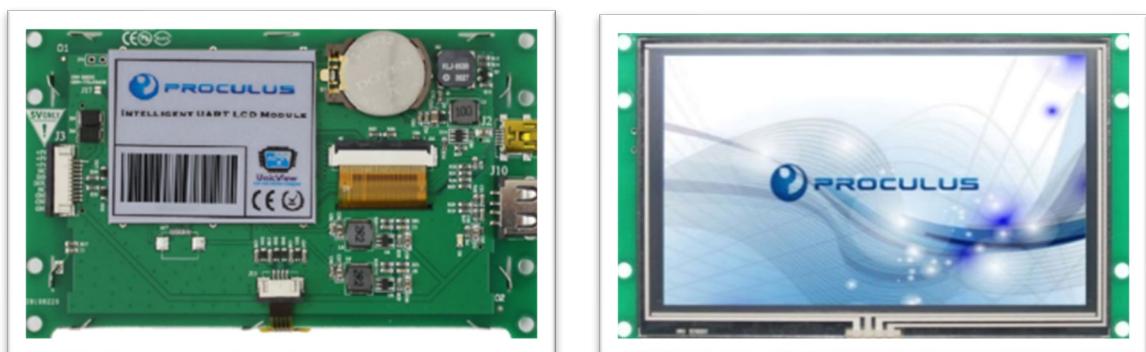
Placa PCB modelo V-80H, montada com componentes
